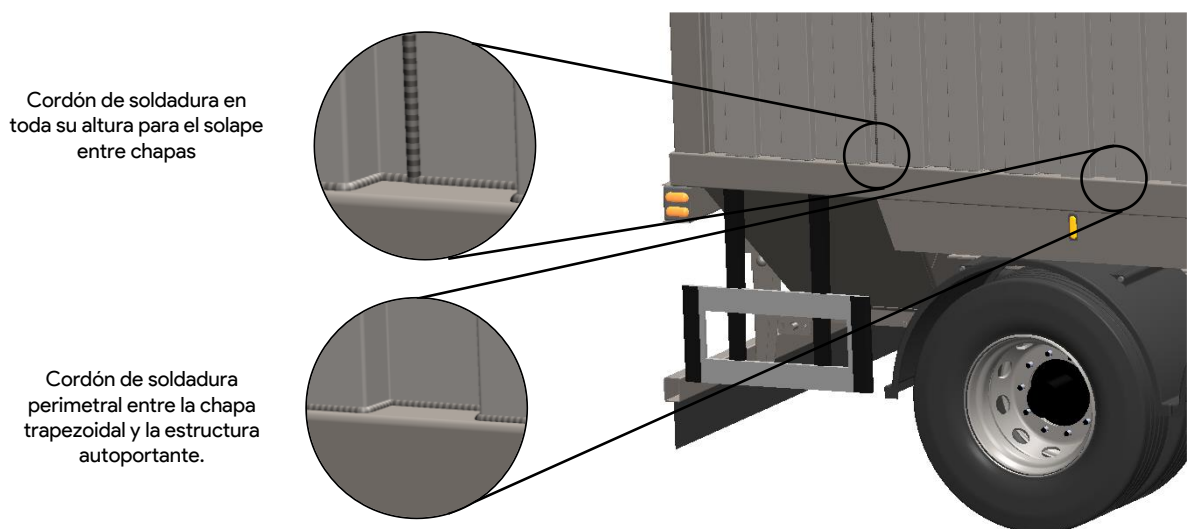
Detalle de cordones de soldadura.
